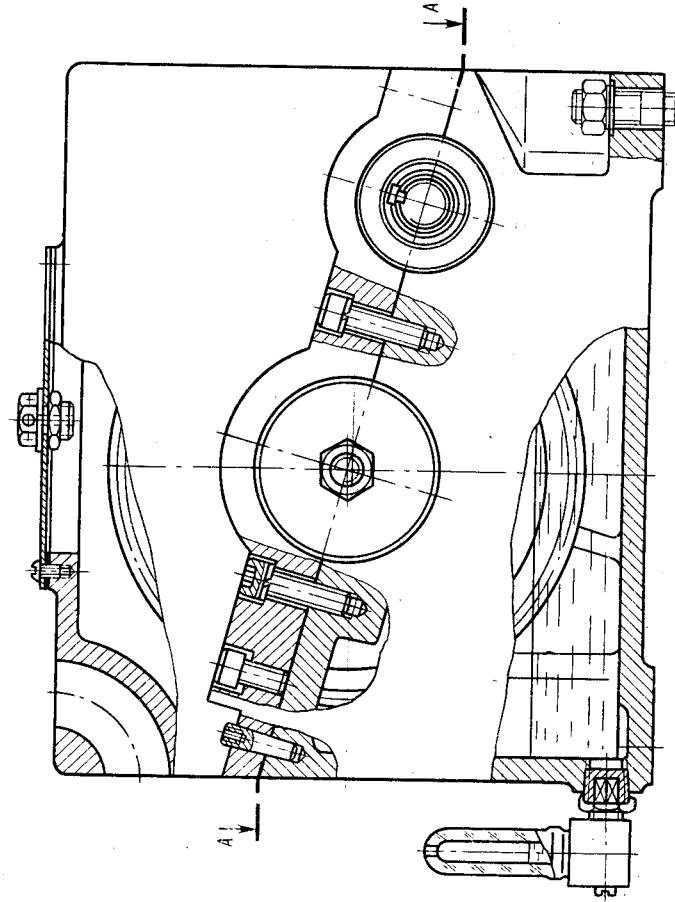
Редуктор цилиндрический одноступенчатый горизонтальный с наклонным разъемом корпуса
